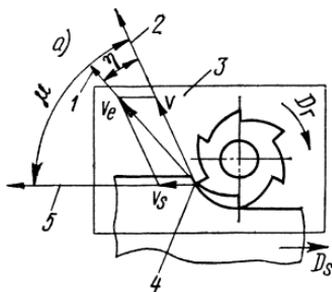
Элементы движений при периферийном фрезеровании:
